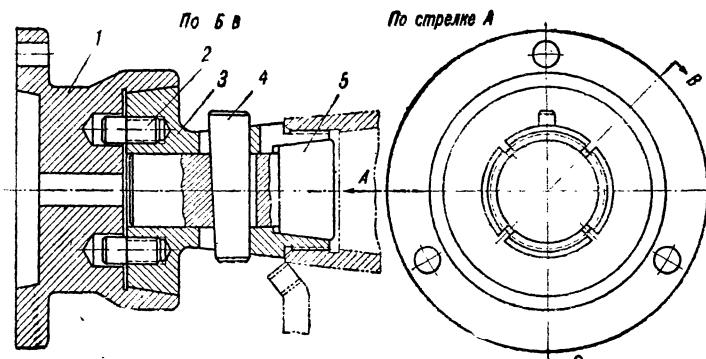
Приспособление для установки длинных изделий по резьбе и центровому отверстию.
